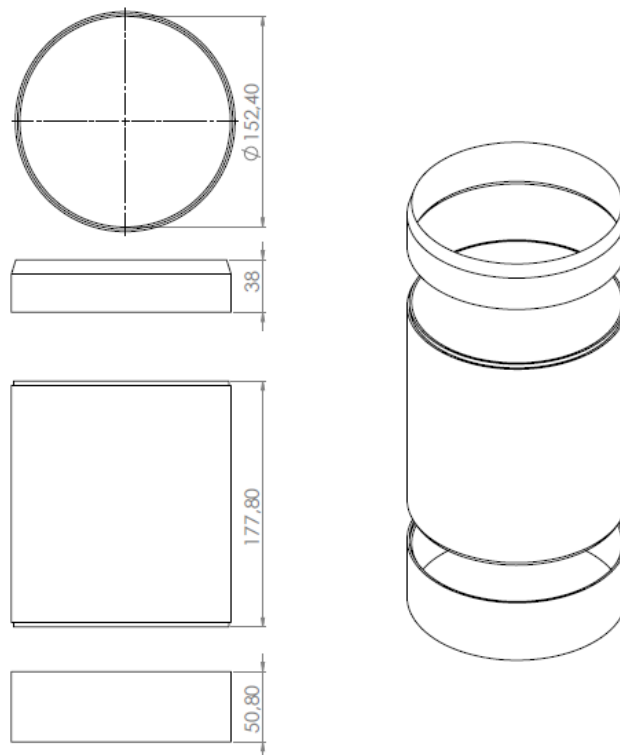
1 Dimensiones del molde de cCBR (en mm)
